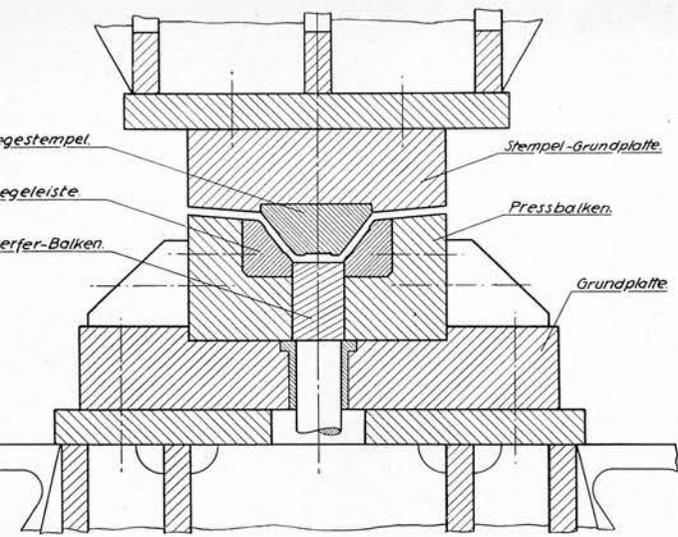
Sicken-Prägwerkzeug, Querschnitt
